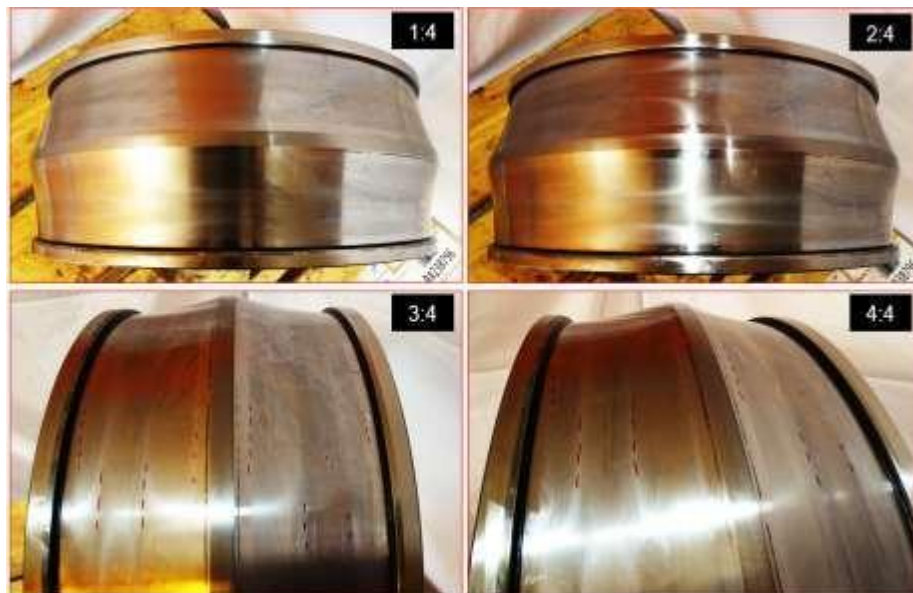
Camino de rodadura de aro interior de rodamiento 231/560
